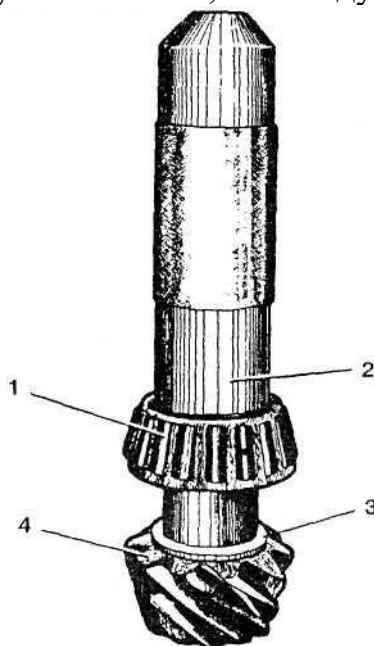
Установка внутреннего кольца заднего подшипника на ведущую шестерню: 1 — внутреннее кольцо заднего роликоподшипника; 2 - оправка А. 70152; 3 - регулировочное кольцо; 4 — ведущая шестерня
